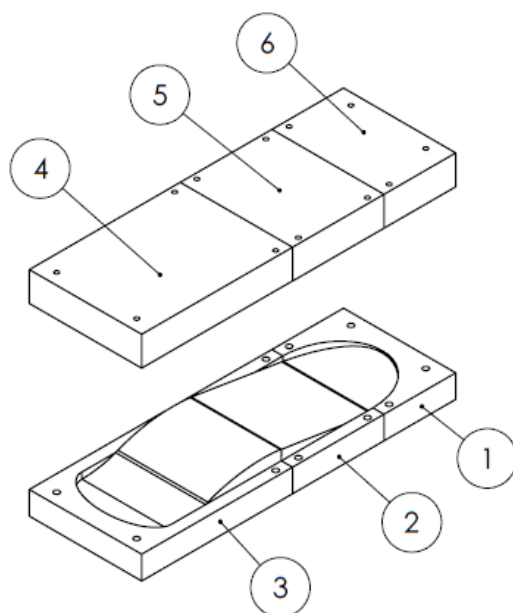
Dibujo de molde superior con dimensiones y componentes Rev. 3
